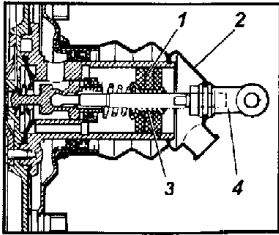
Вакуумный усилитель(фрагмент): 1 -воздушный фильтр, 2 -защитный чехол; 3 -втулка пружины; 4 -толкатель
